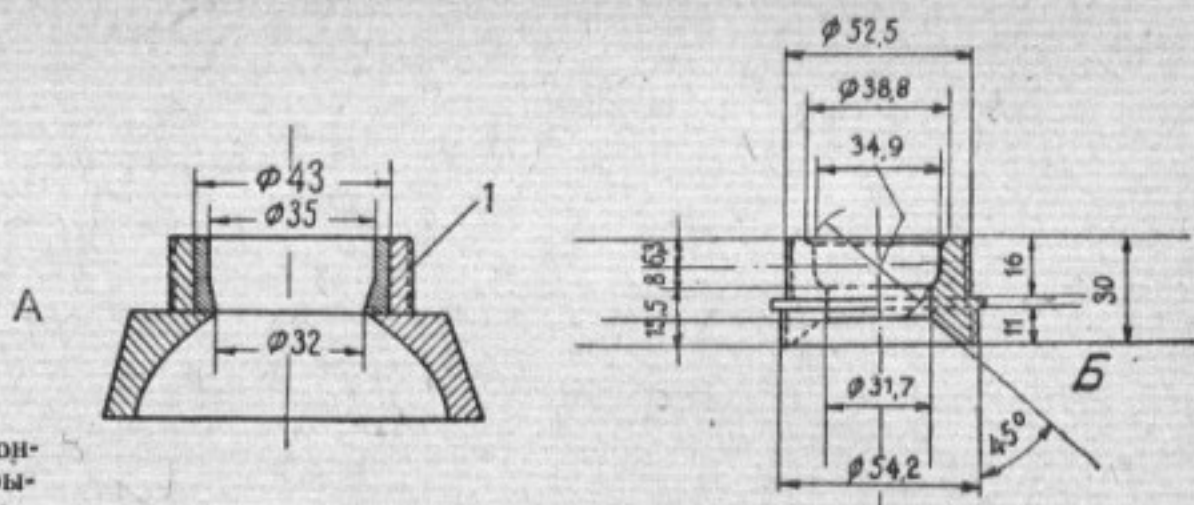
Способы ремонта гнезда верхней крышки коробки передач
